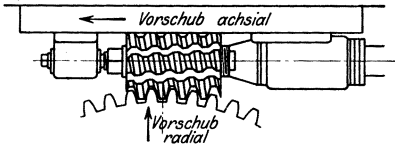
Fräsen eines Schneckenrades mit normalem Schneckenfräser.
